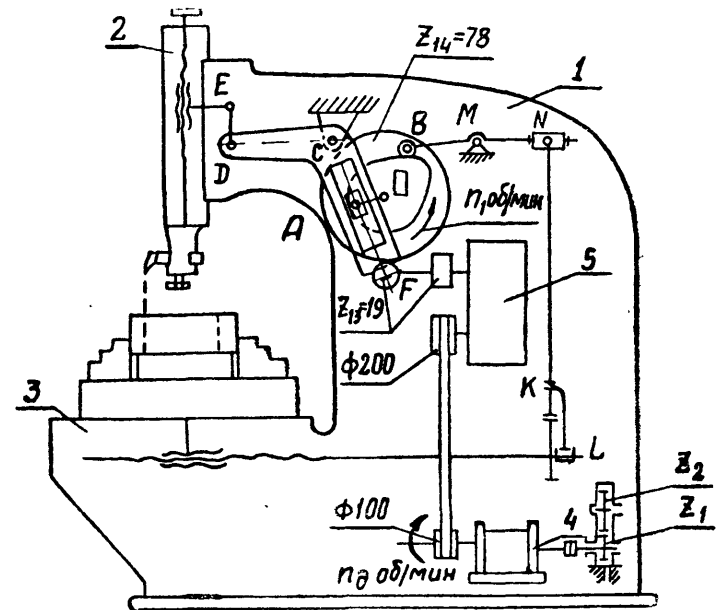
1. Общий вид долбежного станка с качающейся кулисой
